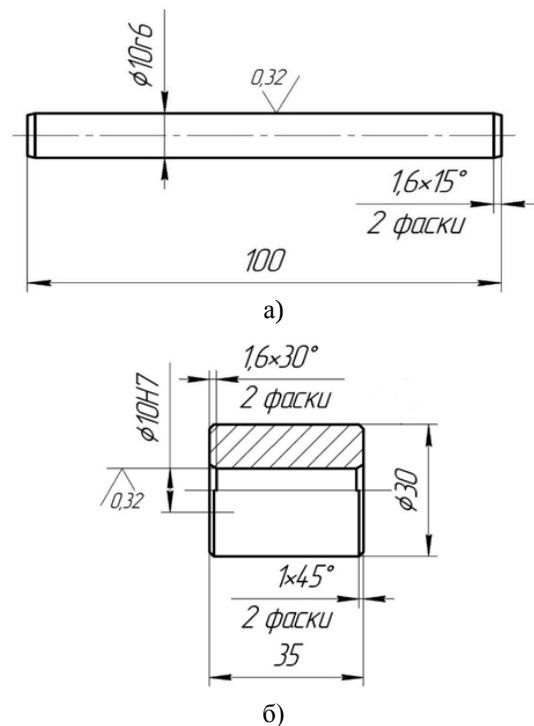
Конструкция образцов деталей соединения с натягом: а – вал; б – втулка
